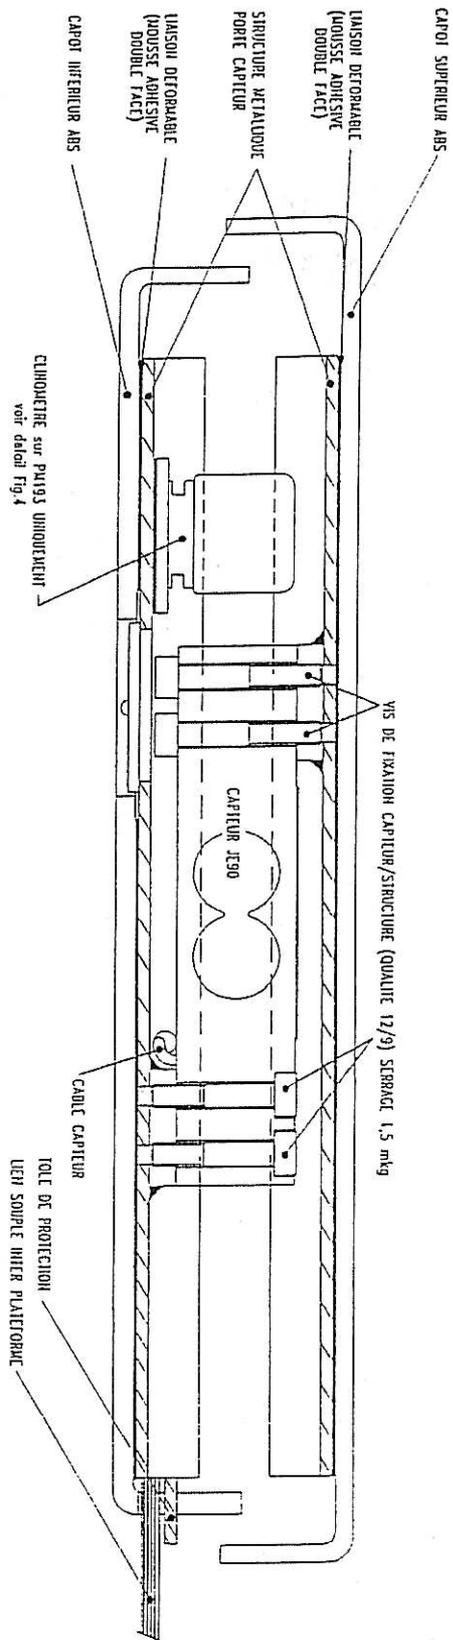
COUPE TRANSVERSALE (BB) D'UNE PLATEFORME
